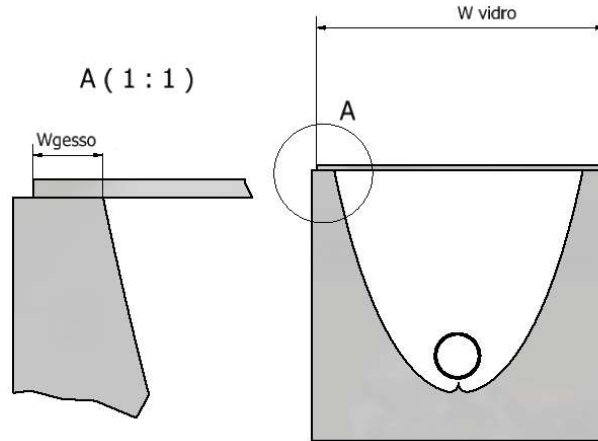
Secção transversal do concentrador e vista de detalhe com espessura de apoio do vidro
